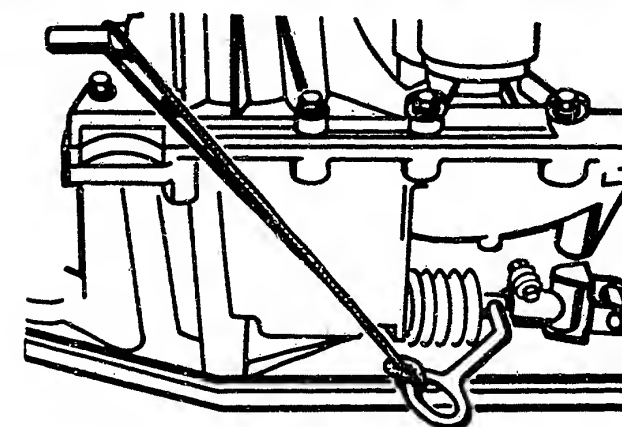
Mit einem selbstangefertigten Hilfswerkzeug lässt sich die Schaltwelle in der richtigen Position halten, bis das Schaltgestänge festgezogen ist.
